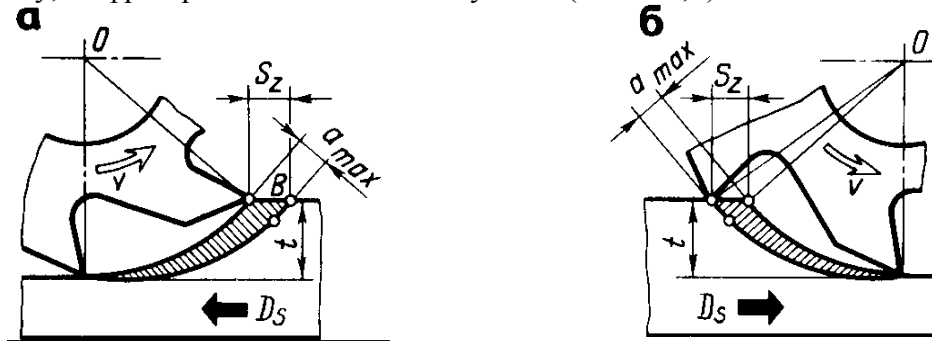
Схемы фрезерования: а) встречное; б) попутное
